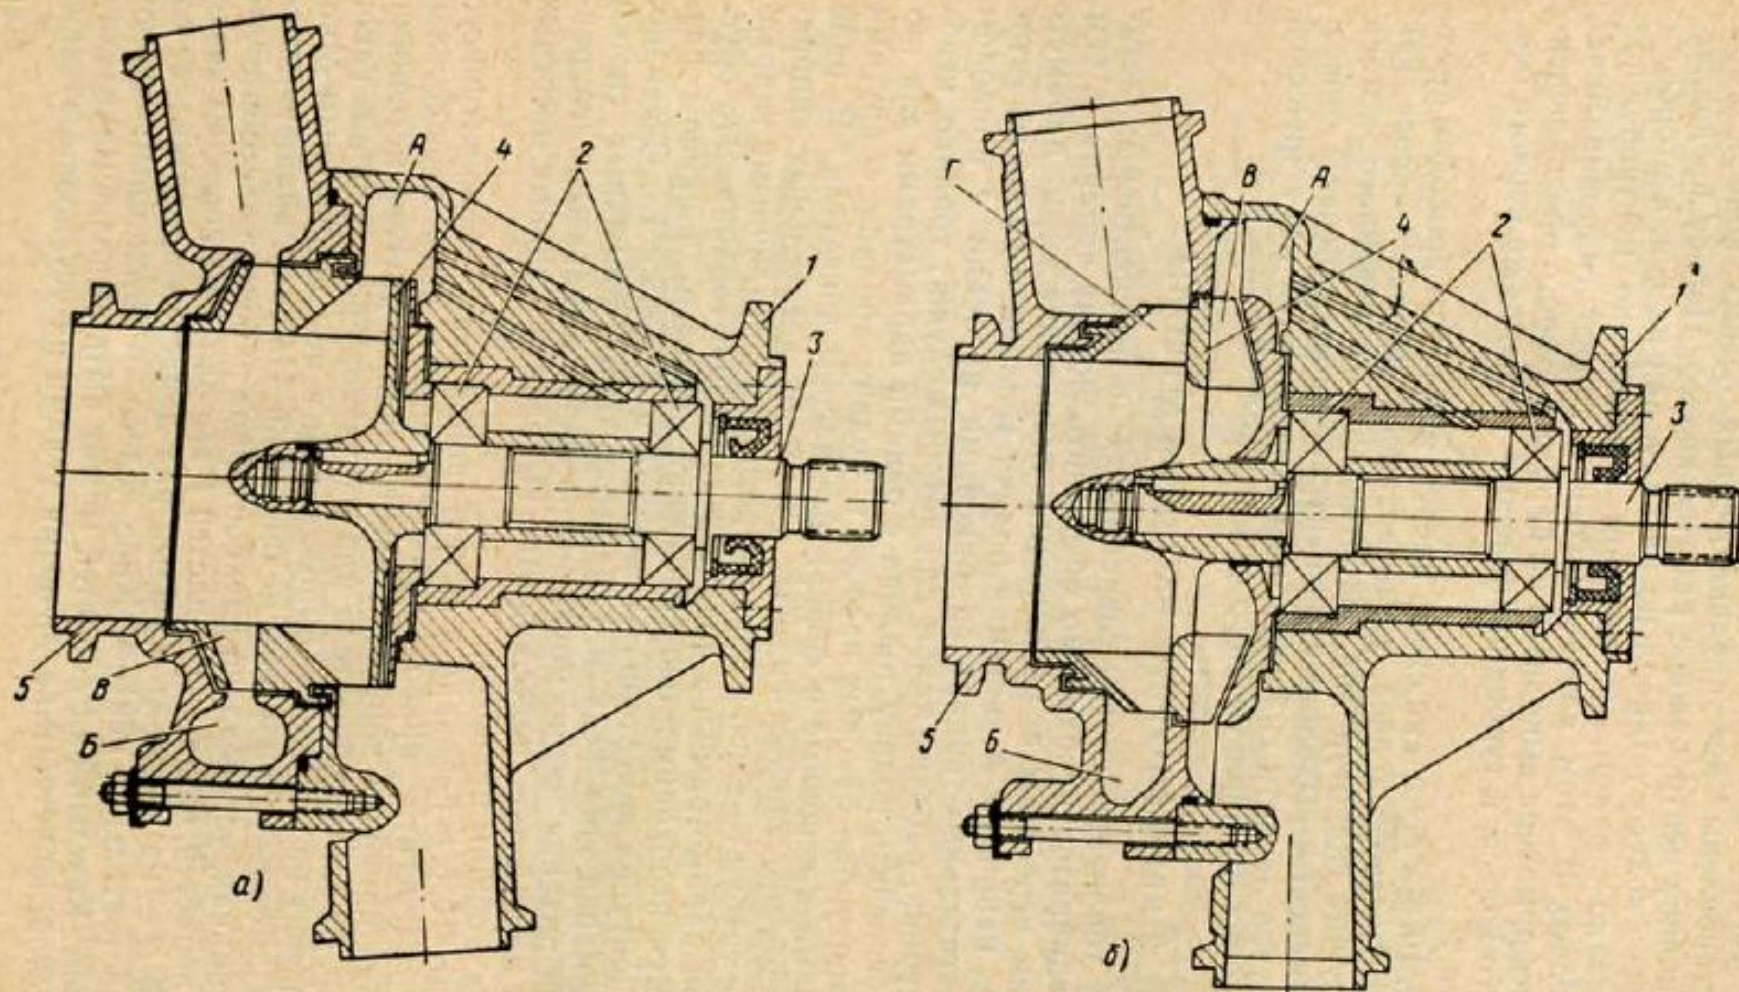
Двухконтурный центробежный насосный агрегат:
